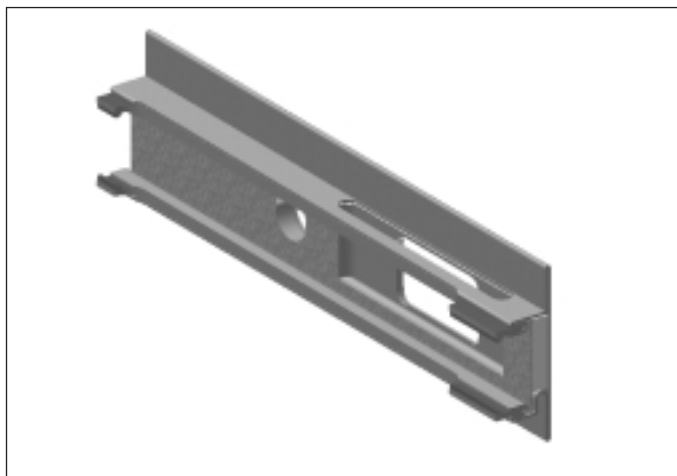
Schlitz für die Bohrschutzplatte (Frästiefe 38 mm)
